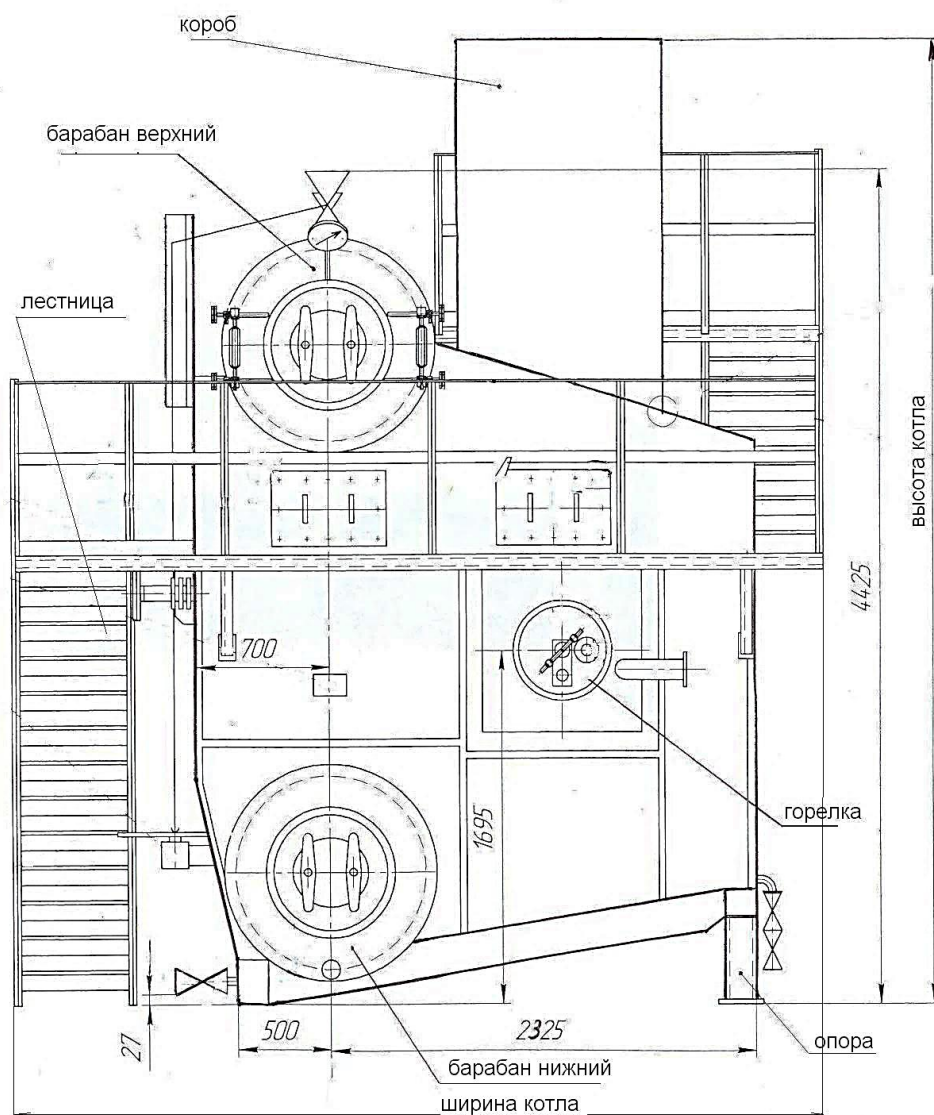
Схема котла ДЕ-25-15-270 ГМ-О
